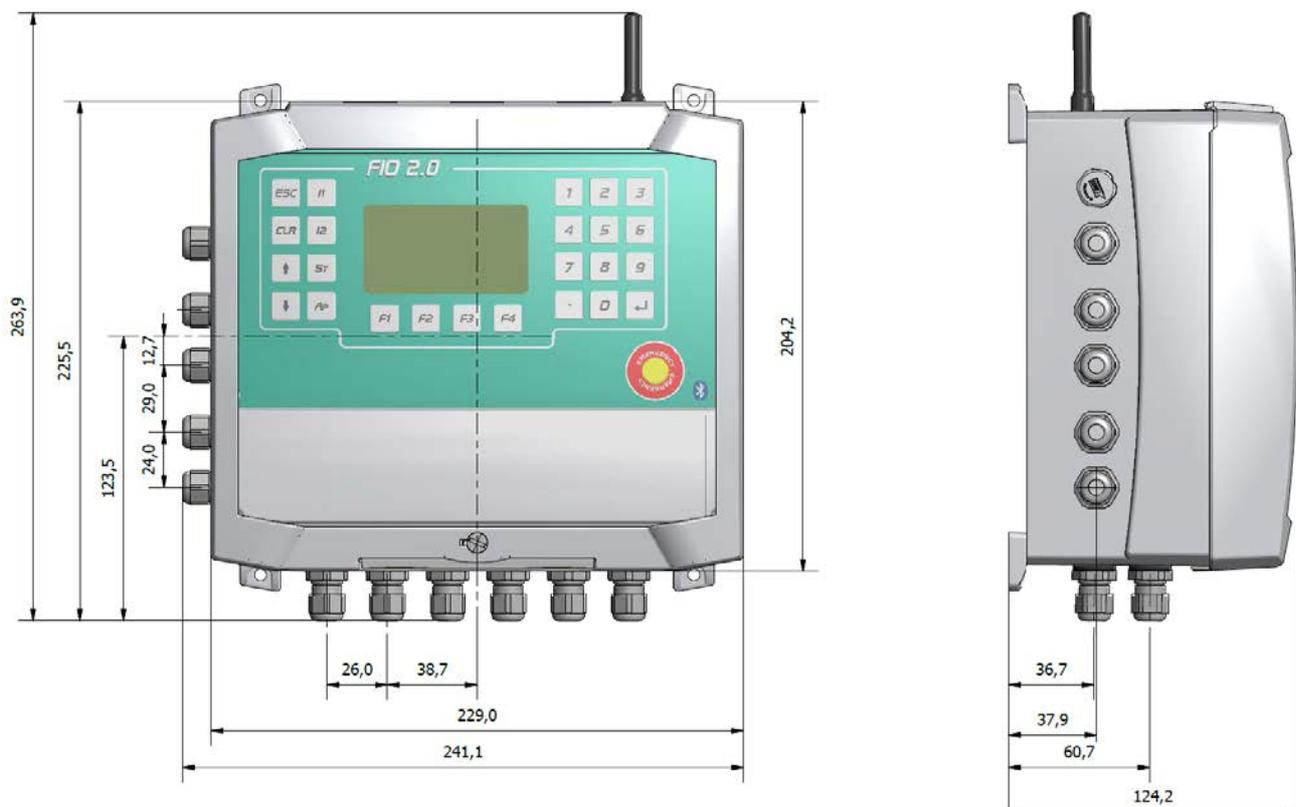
Обзорный вид устройства с закрытой передней дверью
